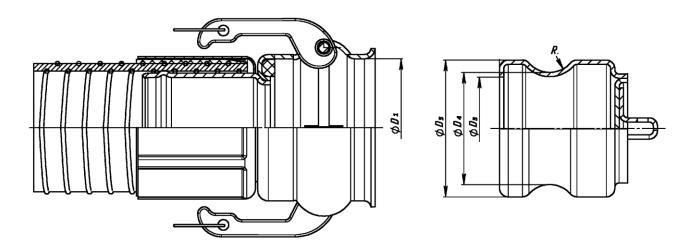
Пристыковочные и присоединительные размеры головок присоединительных с кулачковой муфтой:
